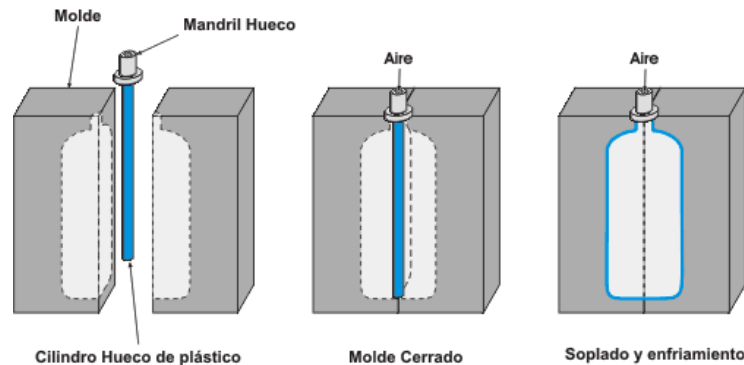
Esquema de moldeo a baja presión. Fuente: 51
